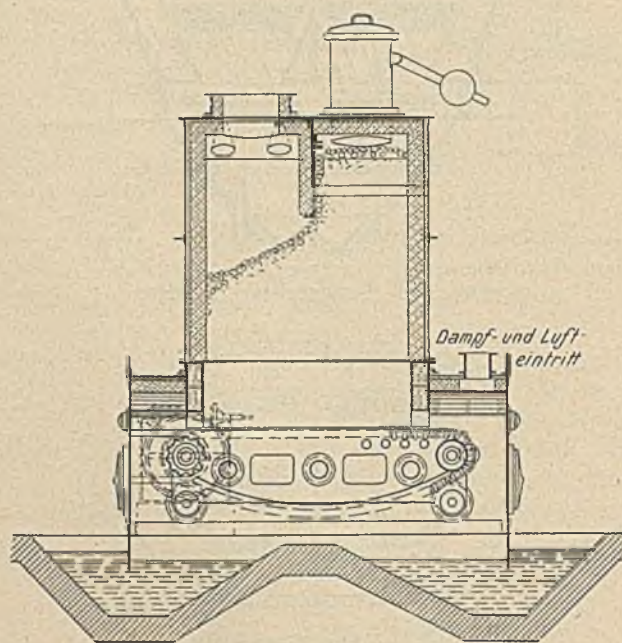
Gaserzeuger mit Kettenrost von Pintsch.
